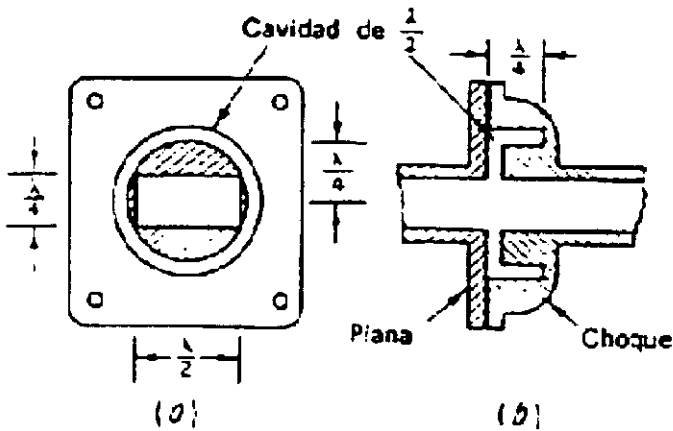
Junta de choque. a) Vista de frente de la brida. b) Sección transversal de la unión de las bridas plana y de choque
